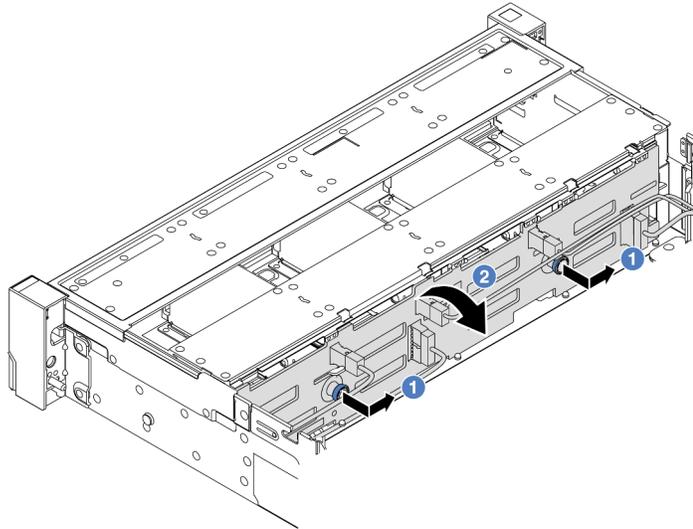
Retrait du fond de panier d'unité 3,5 pouces
